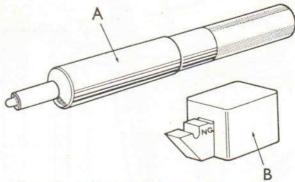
OUTILS DE CONTROLE DE PLAN DE JOINT DE CULASSE
